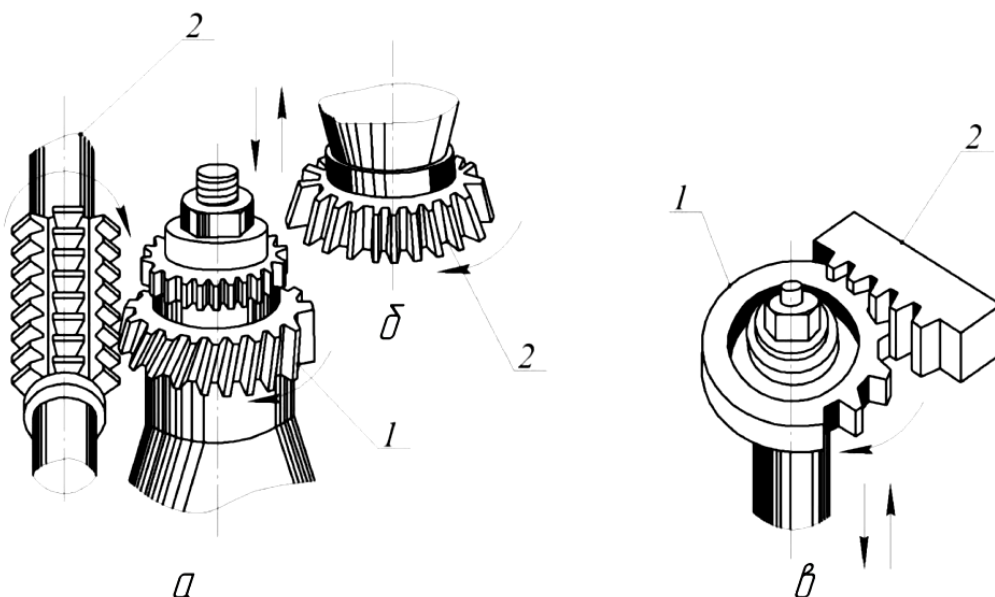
Нарізування зубців методом обкочування: а – черв'ячною фрезною; б – дисковим довб'яком; в) гребінкою; 1 – зубчасте колесо; 2 – інструмент.
